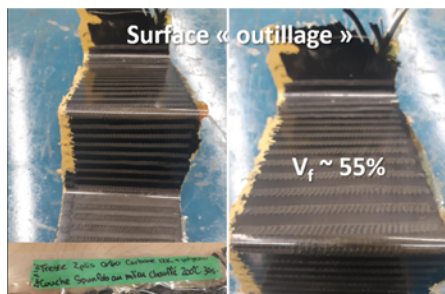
Exemple de pièces composites, avec une section en Z, préformées et moulées par infusion sous vide.
